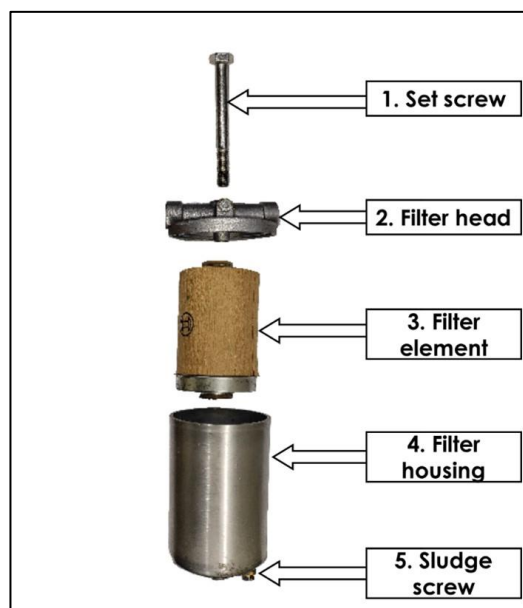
VUE ÉCLATÉE DU FILTRE DE PROTECTION
